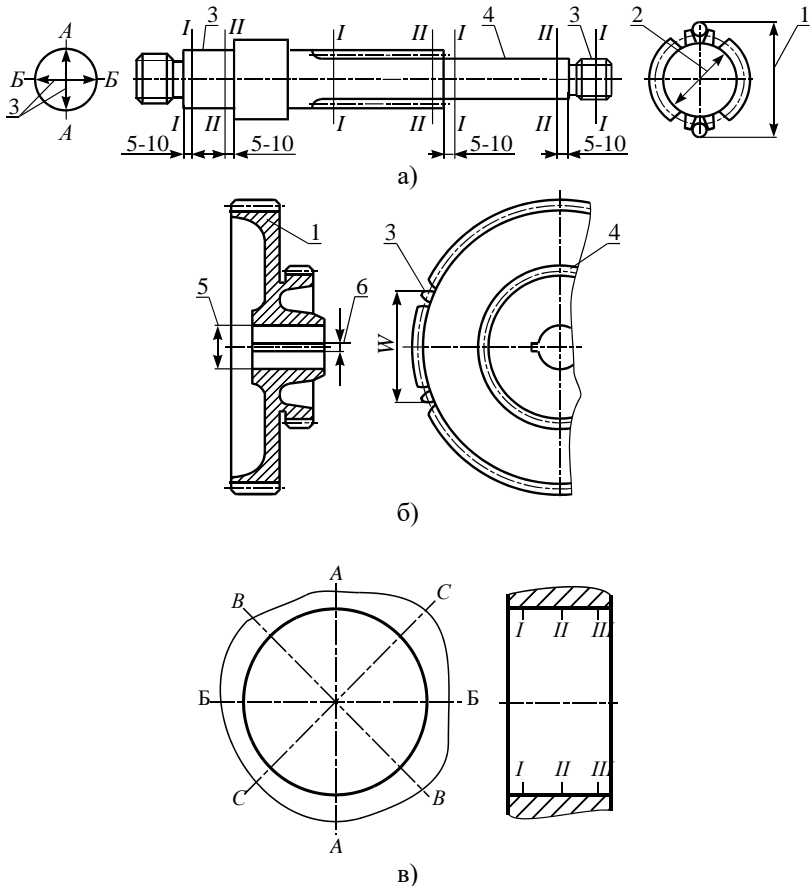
Досліджувана деталь з схематичним зображенням вимірювання геометричних параметрів для дефектування вала (а); шестерні (б) і посадочної поверхні під підшипник кочення (в): А-А, Б-Б, В-В, С-С – площини вимірювання; I-I, II-II, III-III – перерізи вимірювання
